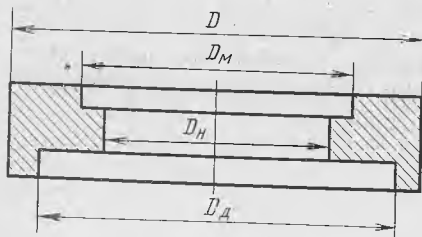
Центрирующее кольцо: D — наружный диаметр кольца; D_M — диаметр внутреннего диаметра кольца для установки пресс-формы; D_H — диаметр наружного пояса свернутой пластины; D_d — диаметр нижнего внутреннего кольца для установки на наружный диаметр детали
